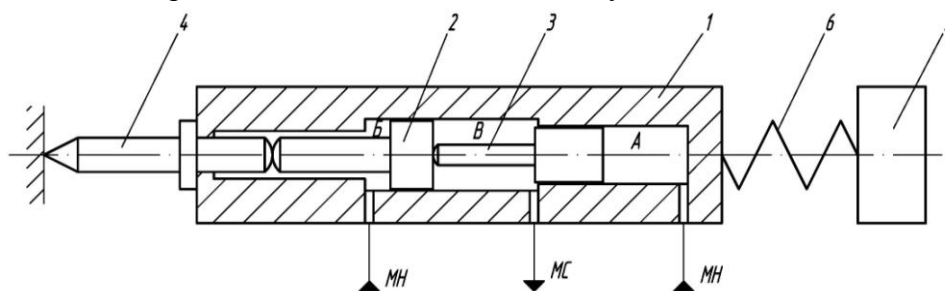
Схема гидравлического отбойного молотка типа МО-9Г: корпус 1, боек 2, плунжер 3, инструмент 4, рукоятка 5 с пружиной 6; А – камера рабочего хода, Б – камера обратного хода, В – вспомогательная камера
